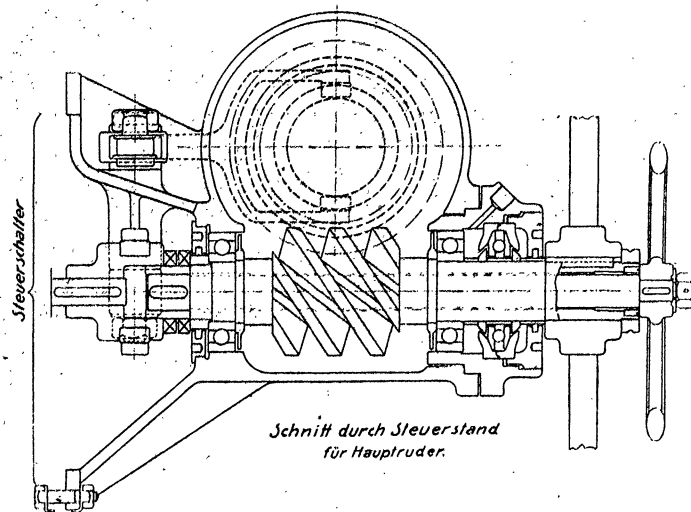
a. Steuerstand für Rudermaschinen mit unmittelbarer Fernsteuerung der Germaniaerft Kiel
